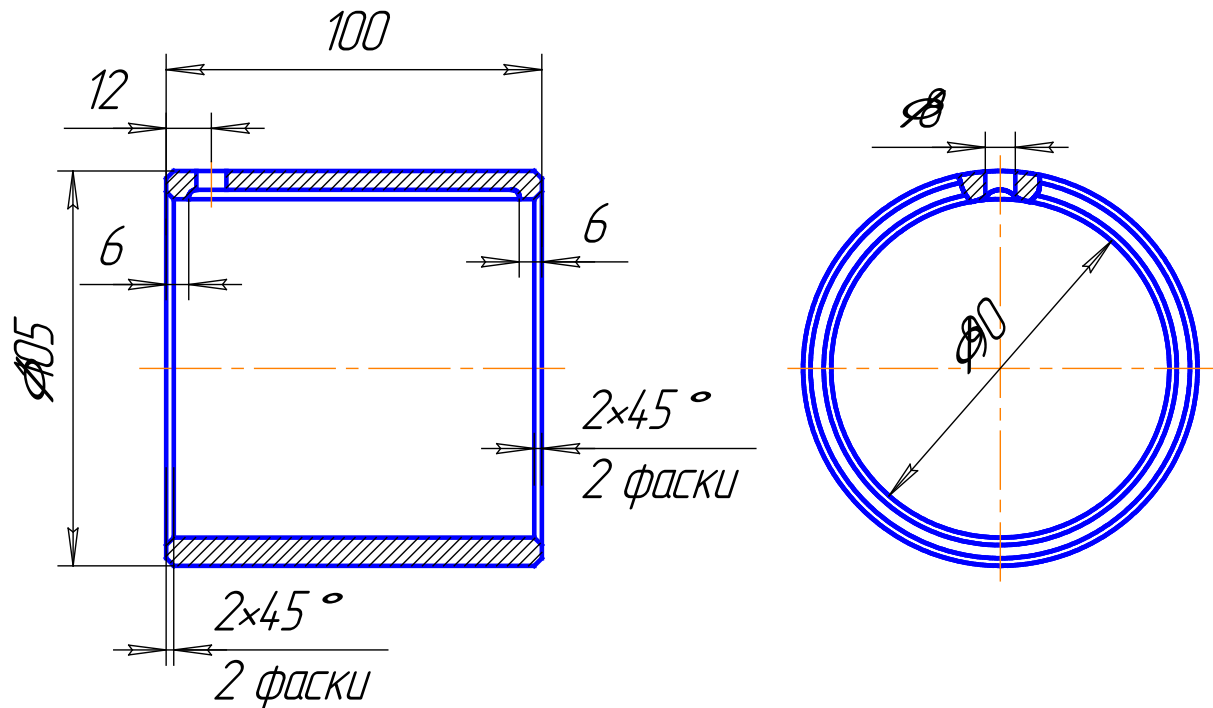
Ескіз втулки 90×100 підшипника ковзання
